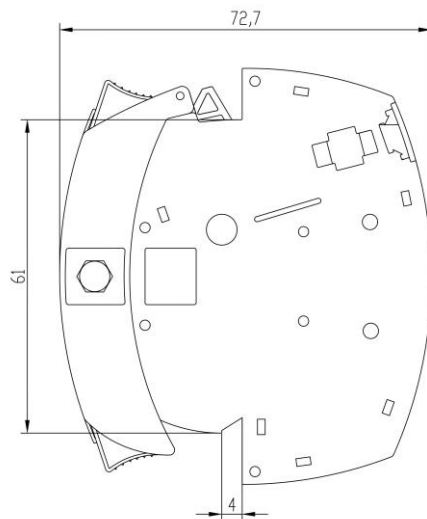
Общий вид базового блока ЭПББ с установленной рабочей крышкой ЭПРК. Вид сбоку.
